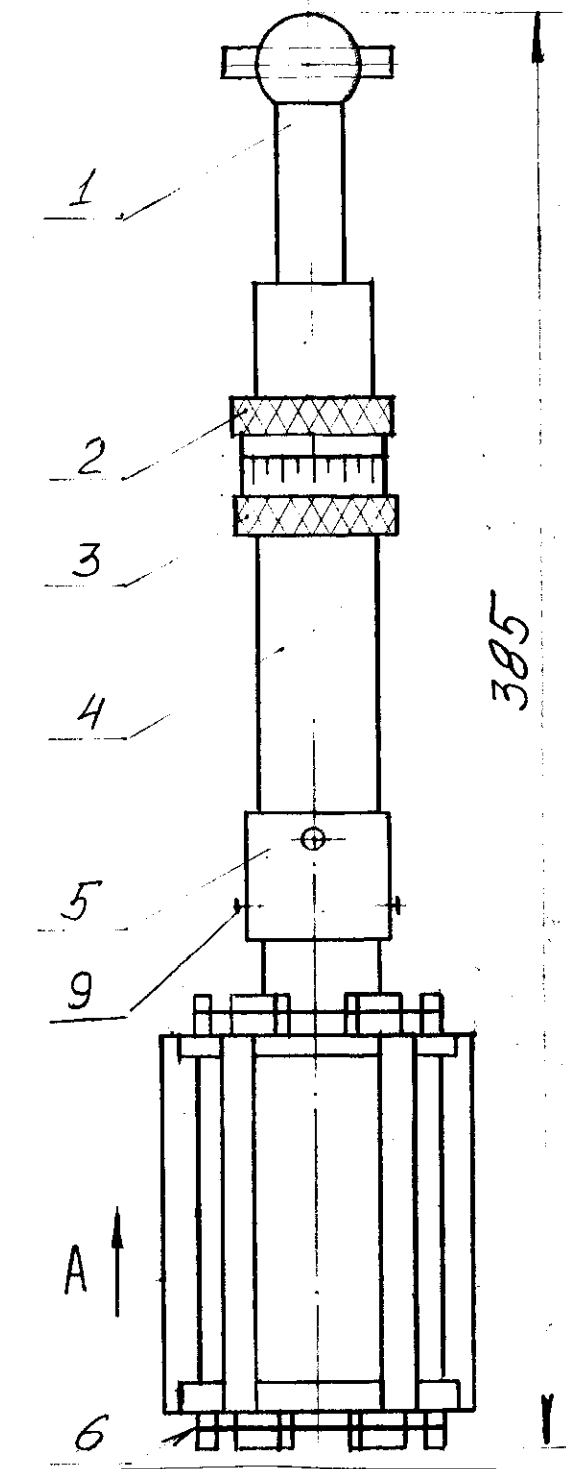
Крепление установки УХ на блоке цилиндров
